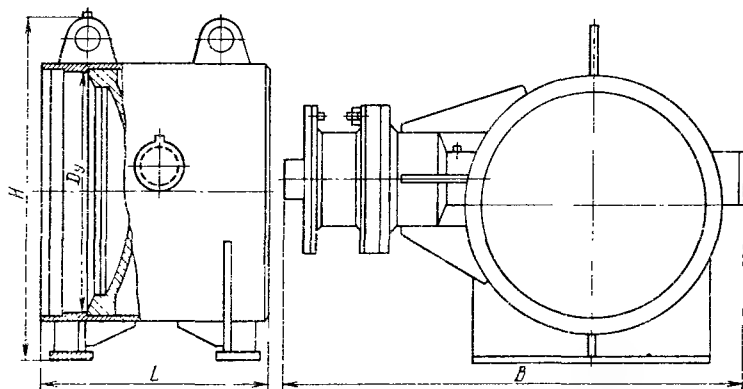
Клапан обратный поворотный с демпферным устройством
